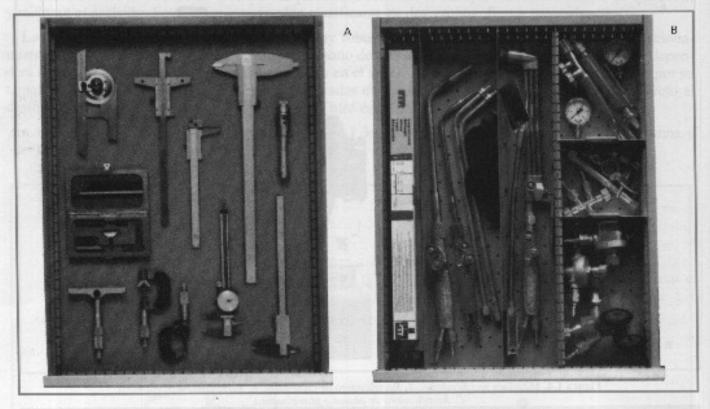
A. Juego de medición. B. Juego de soldadura.
